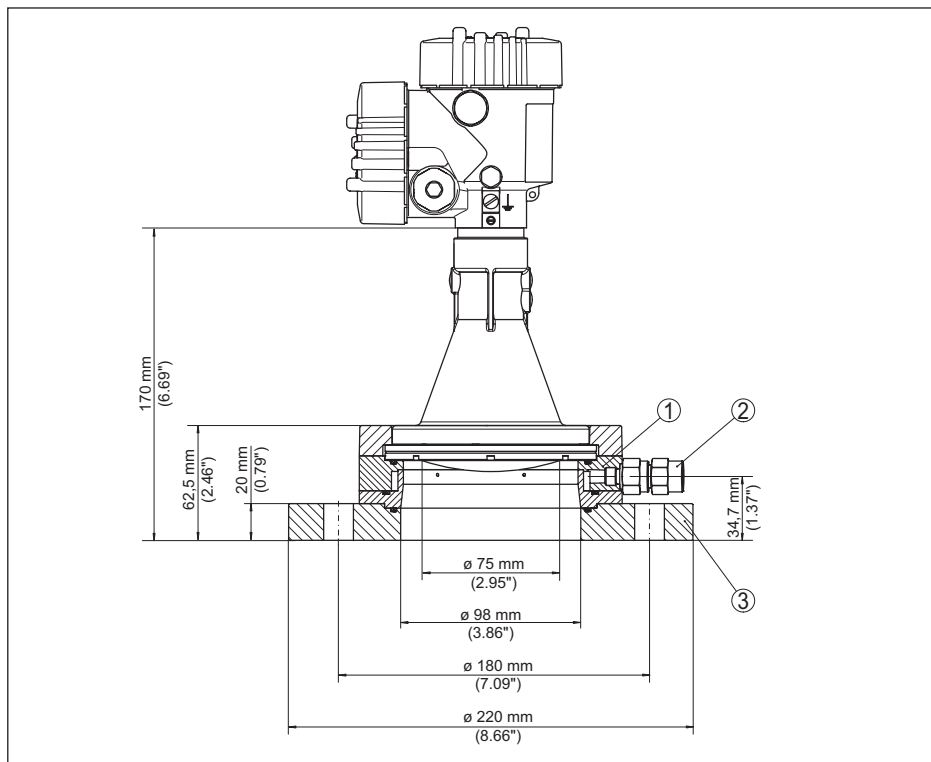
VEGAPULS 6X, flange adaptador e conexão de ar de limpeza DN 100 PN 6
